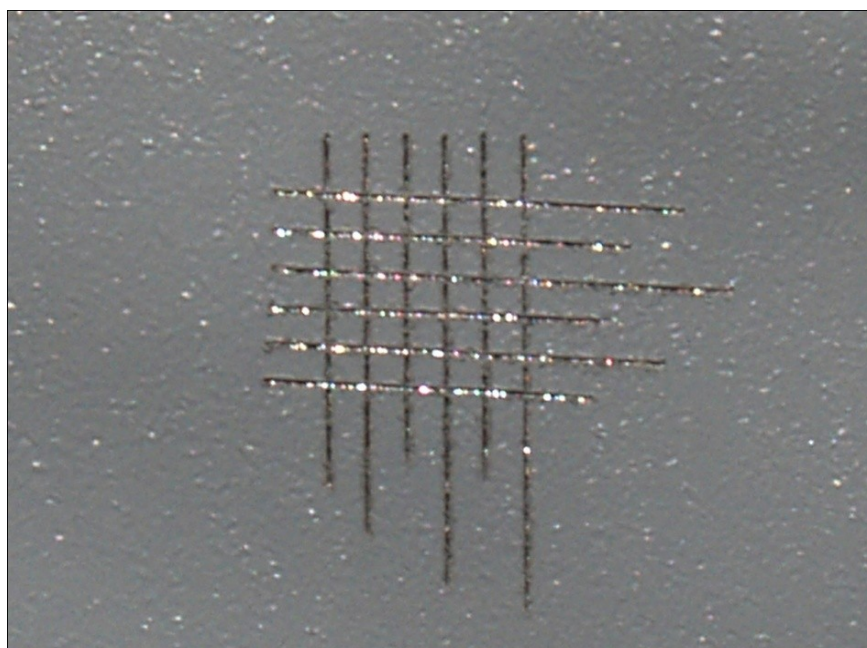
sada pro mřížkovou zkoušku TQC SP3100
